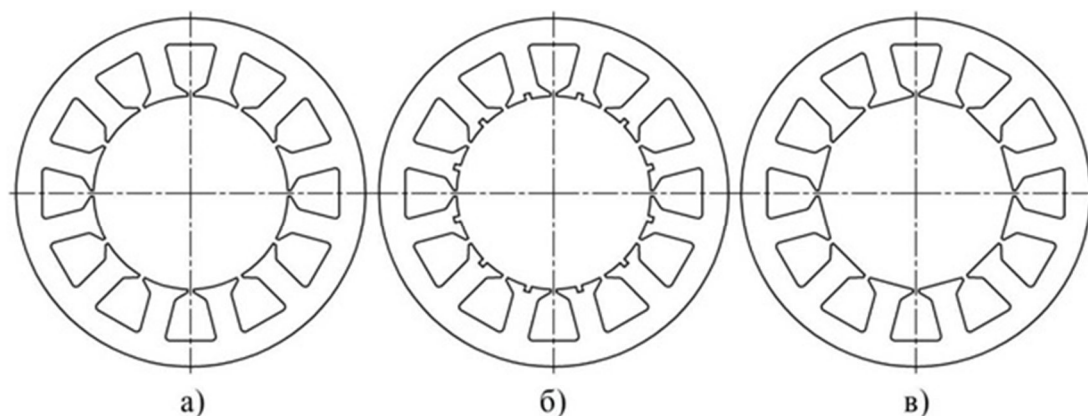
Конструкции статоров синхронных машин с дробными зубцовыми обмотками
